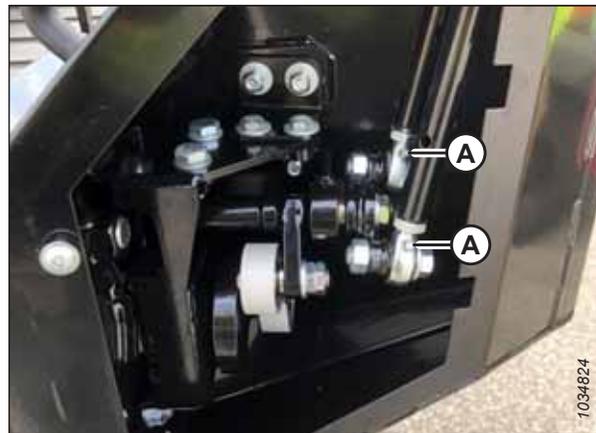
Graissage des embouts sur les tiges-poussoirs des couteaux verticaux
